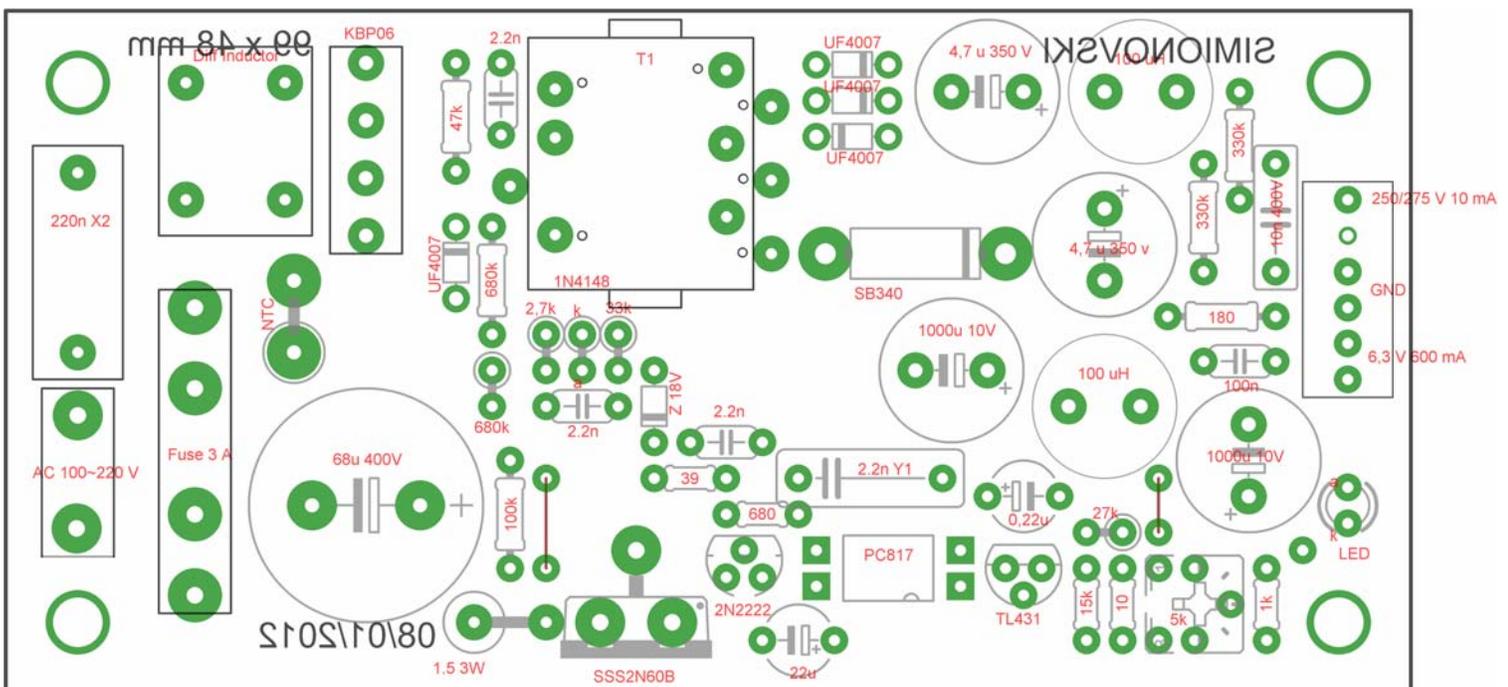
Disposição dos componentes sobre a placa de circuito impresso.
